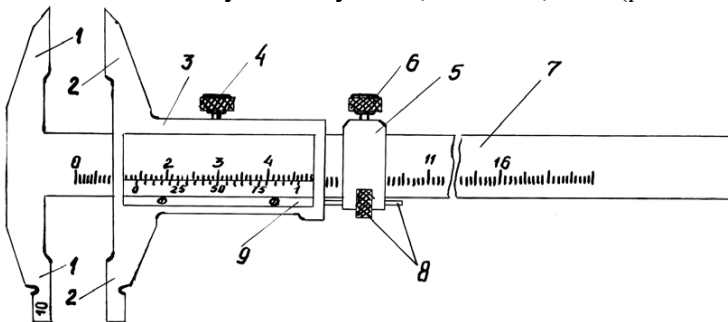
Штангенциркуль ШЦ-II: 1 – нерухомі вимірювальні губки; 2 – рухомі вимірювальні губки; 3 – рамка; 4 – затискач раки; 5 – рамка мікрометричної подачі; 6 – затискач рамки; 7 – штанга; 8 – гайка і гвинт мікрометричної подачі рамки; 9 – ноніус
